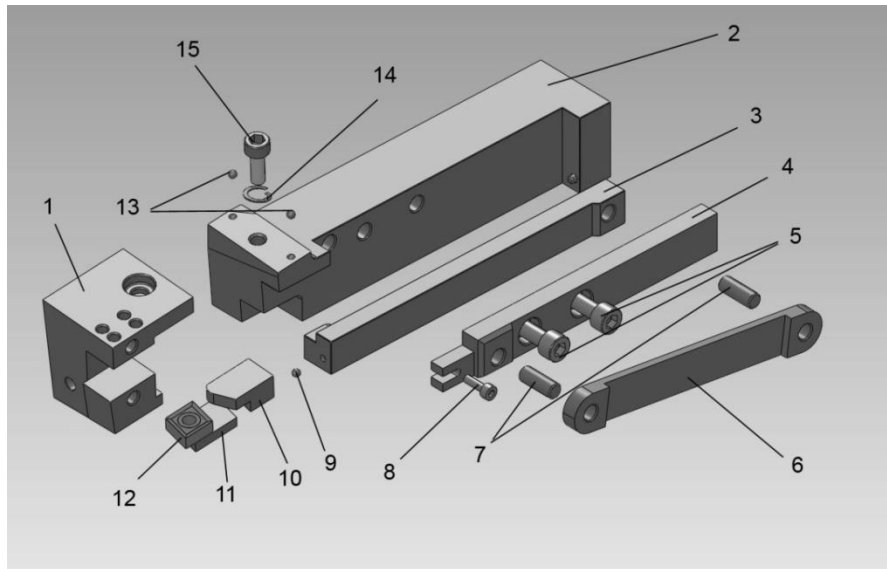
Вимірювальний токарний різець: 1 – головка; 2 – корпус; 3 – нижня планка; 4 – верхня планка; 5,8 – болти; 6 – планка тензодатчика; 7 – вісь; 9,13 – опорні кульки; 10 - верхня прокладка; 11 - нижня прокладка; 12 – різальна пластина; 14 – пружина; 15 – натискний болт
